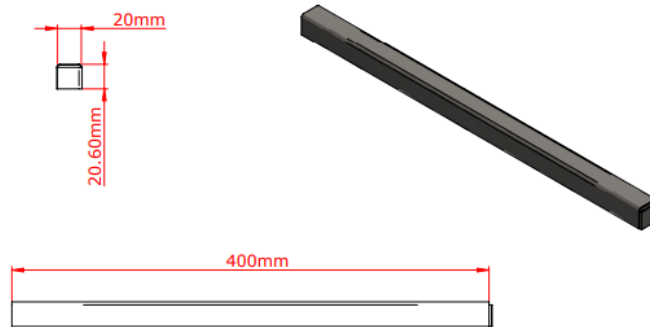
Sección 2 de la puerta - Detalle de las medidas
